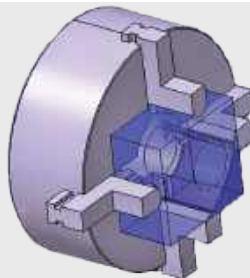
Установлення заготовки некруглої форми в чотирикулачковому патроні
